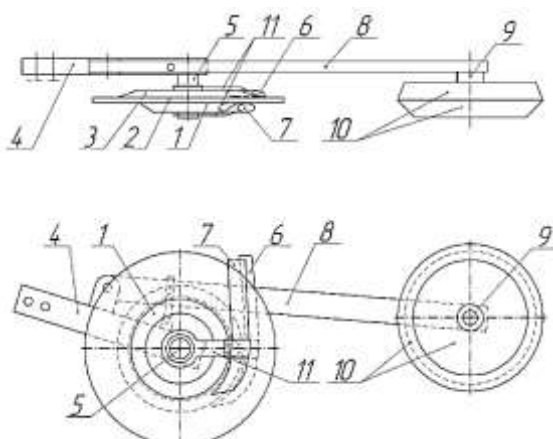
Комбинированный однодисковый сошник с двухсторонними ребрами-бороздкообразователями с разными диаметрами и нулевым углом атаки дисков: 1, 3 – уплотнители; 2 – плоский диск; 4 – корпус; 5, 9 – оси; 6 – семянаправитель; 7 – туконаправитель; 8 – поводок; 10 – прикатывающий каток; 11 – пластины
